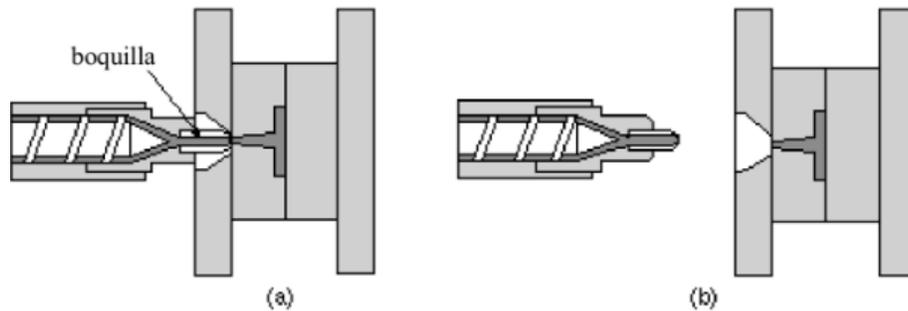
A) boquilla con extrusora en posición del proceso, b) boquilla en etapa de purga (Castro *et al.* 2010)
